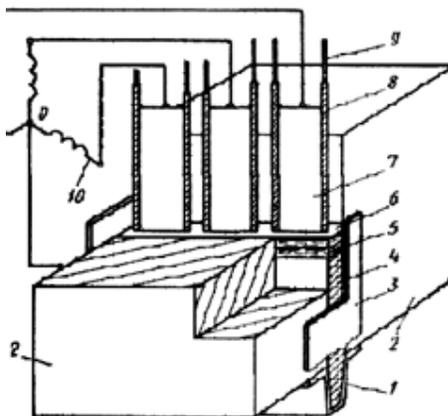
Схема ЭШС плавящимся мундштуком (ШМ) прямолинейных стыков: 1 — медный кокиль для начала сварки; 2 — свариваемые заготовки; 3 — устройство для удержания металлической и шлаковой ванны в зазоре при сварке и формировании шва (охладитель); 4 — шов; 5 — металлическая ванна; 6 — шлаковая ванна; 7 — плавящийся мундштук; 8 — спираль из проволоки или свальная трубка для подачи проволоки к месту сварки; 9 — электродная проволока; 10 - вторичная обмотка сварочного трансформатора
